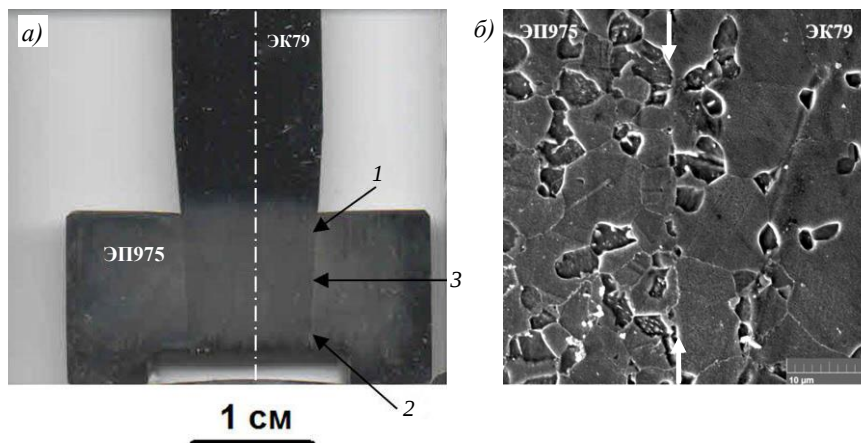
Образцы после сварки давлением: а – общий вид; б – структура в зоне твердофазного соединения [11]
